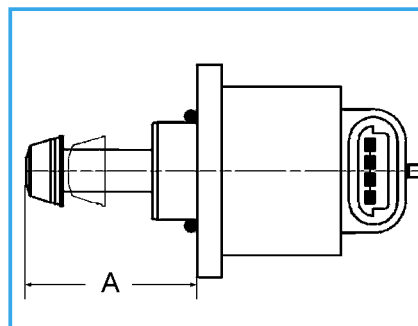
A – Medida de ajuste para el montaje provisional 35 a 36 mm
